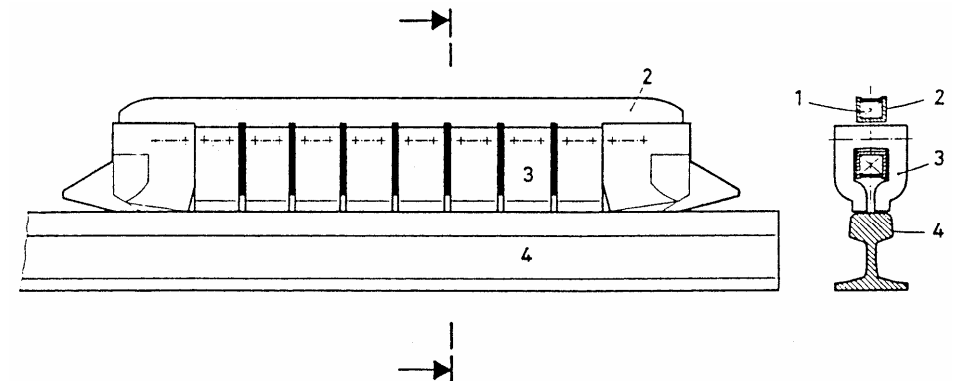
Prinzipieller Aufbau der Magnetschienenbremse
